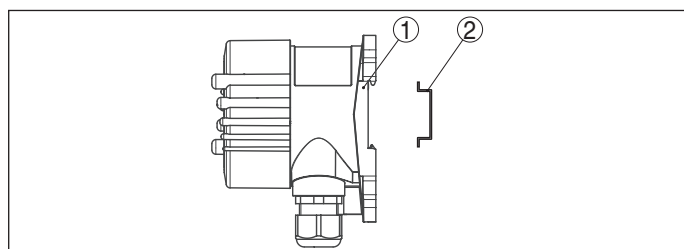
VEGADIS 81 и 82 с пластиковым корпусом для монтажа на несущей рейке
